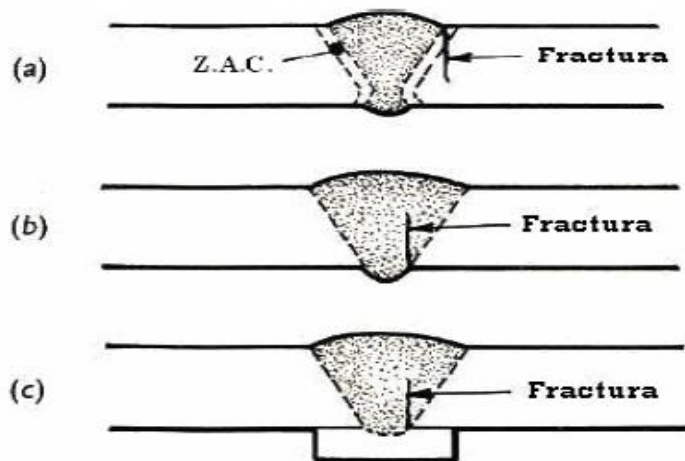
Modos típicos de fractura en soldadura a tope.
